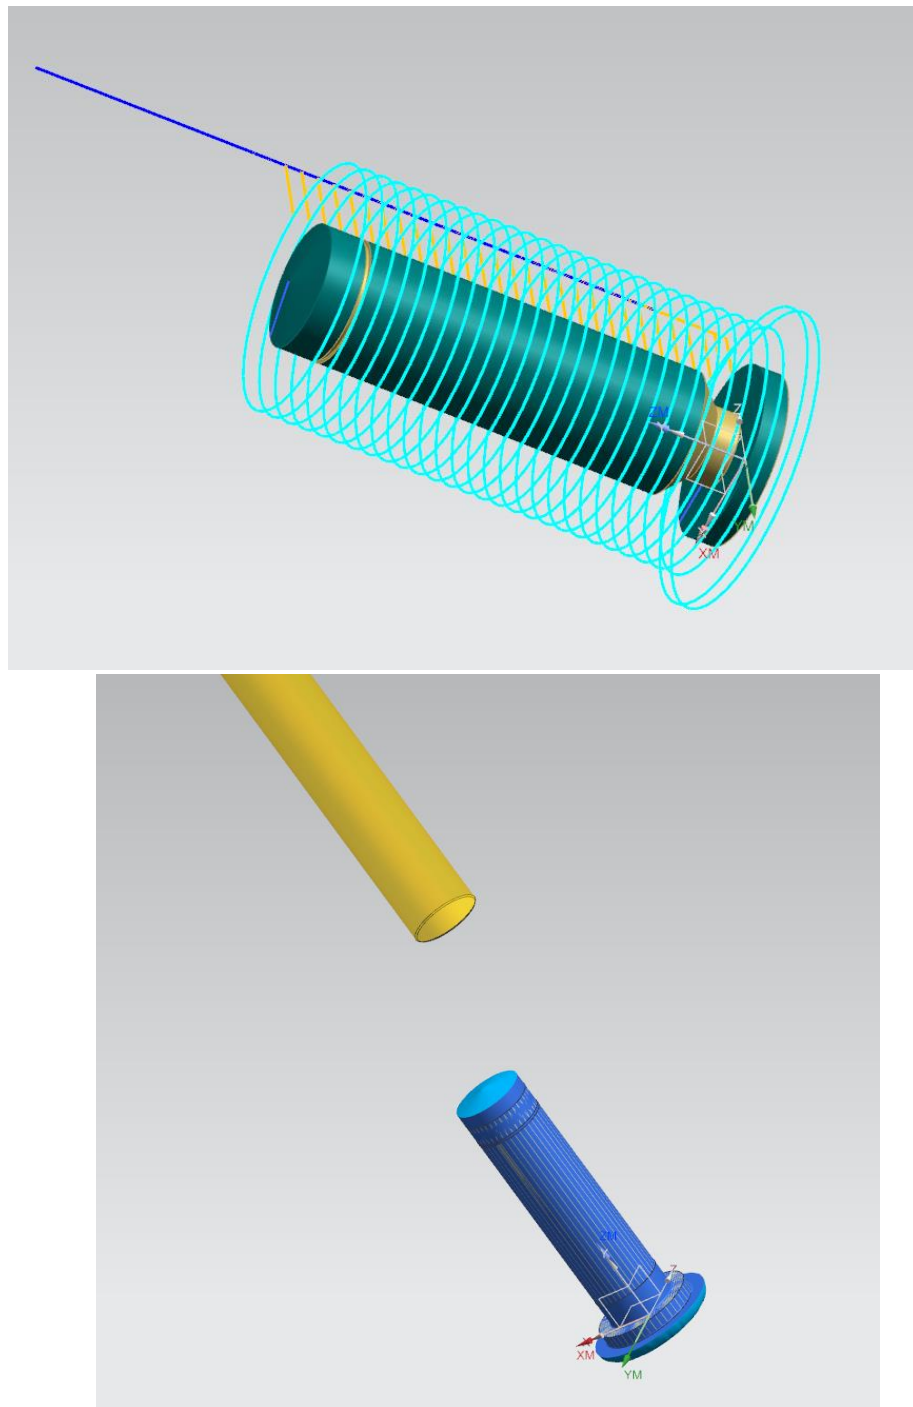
Фрезерування зовнішніх поверхонь
